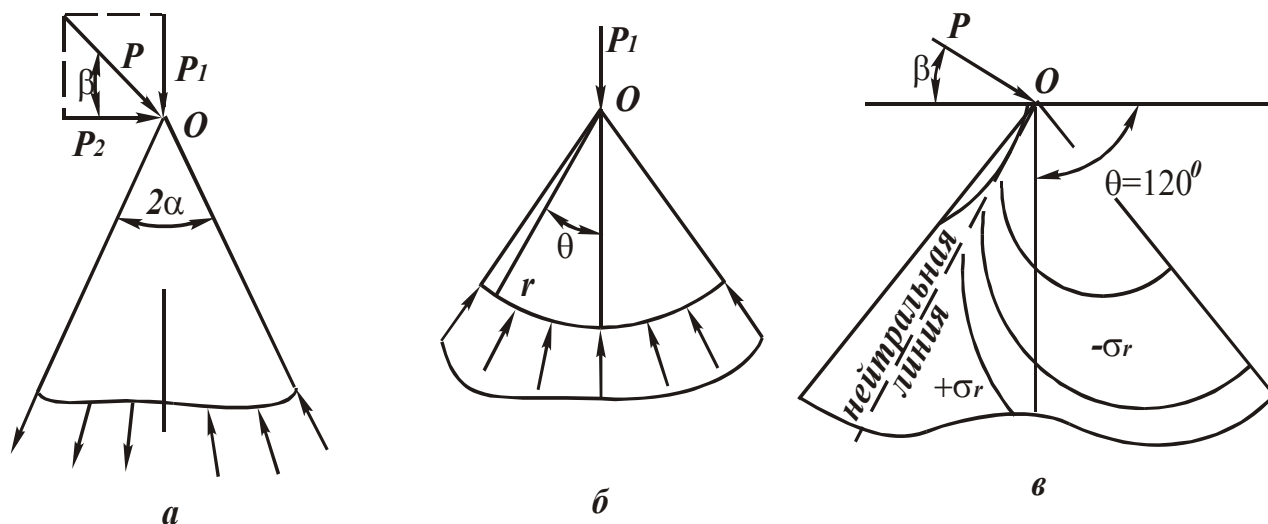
Схемы расчета напряжений в режущем клине инструмента.
